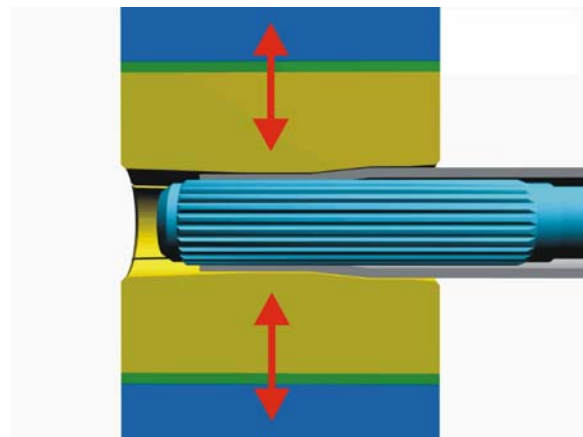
Vorschubkneten mit (verzahntem) Innenwerkzeug
